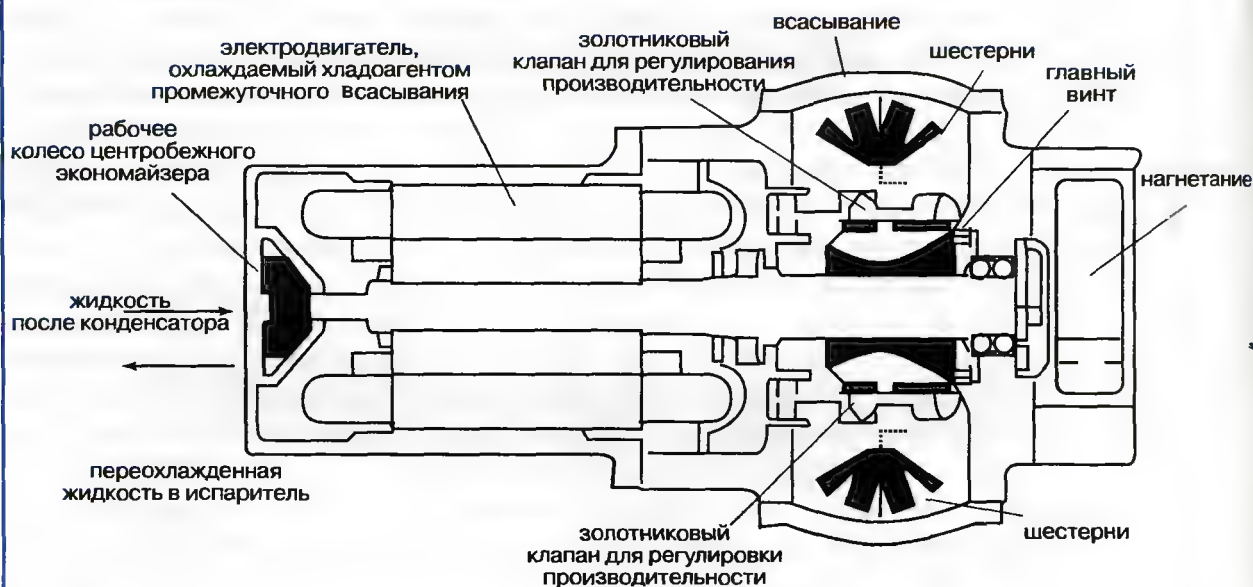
Устройство полугерметичного одновинтового компрессора
